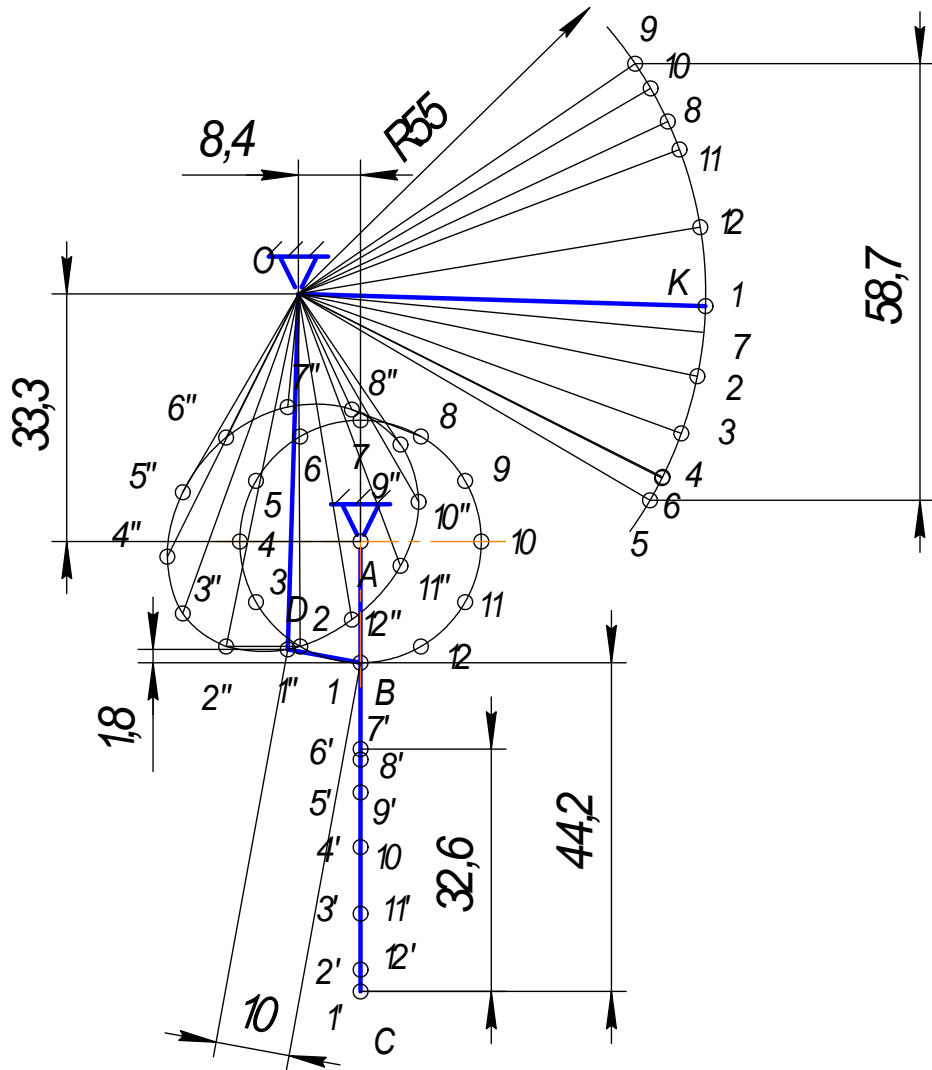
Кінематична схема механізму ниткопритягувача машинки 224-го класу
